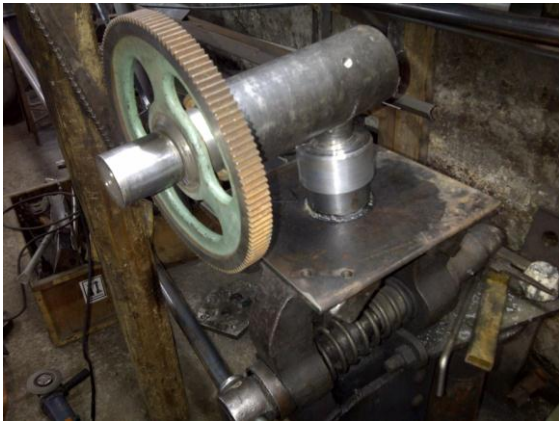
Soldadura de porta carbones con porta aspas.
